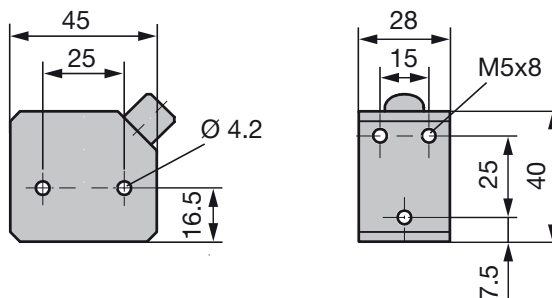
Dimensioni di ingombro datore di posizione BTL5-P-4500-1
